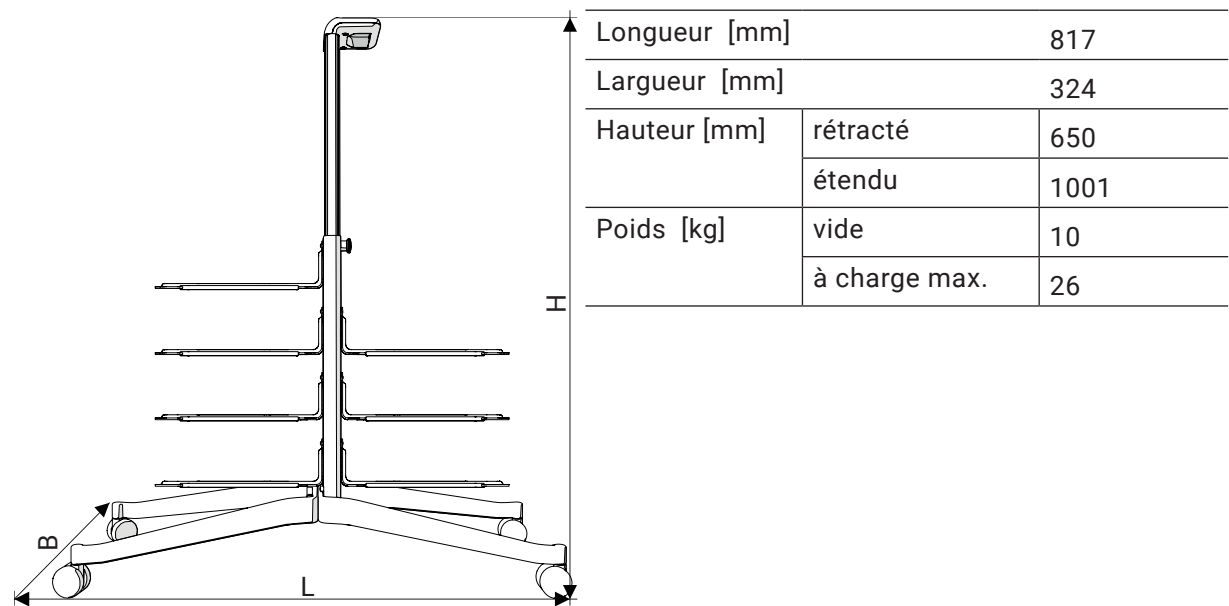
Dimensions du Caddy de bureau Workplace double face
